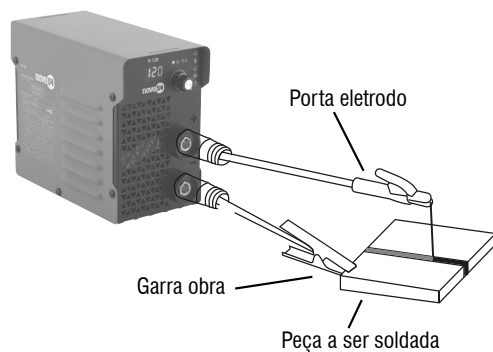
Montagem dos cabos de solda para soldagem de Eletrodo Revestido (MMA)
